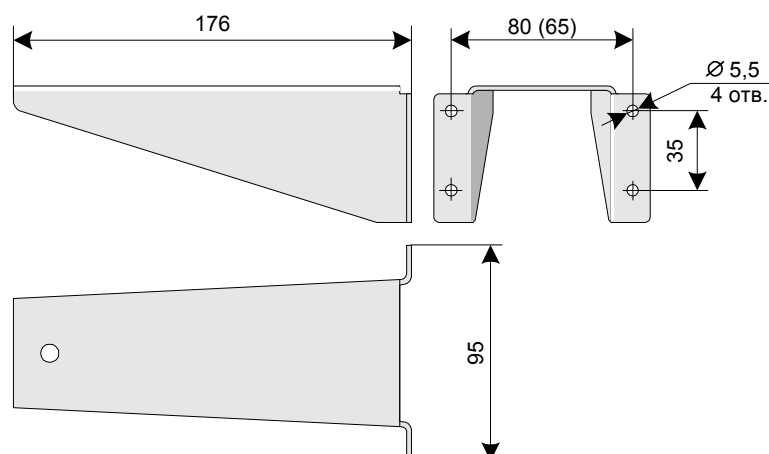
Кронштейн для крепления камер в металлическом корпусе.
